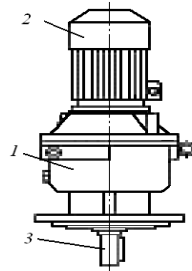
Загальний вигляд мотора-редуктора:
